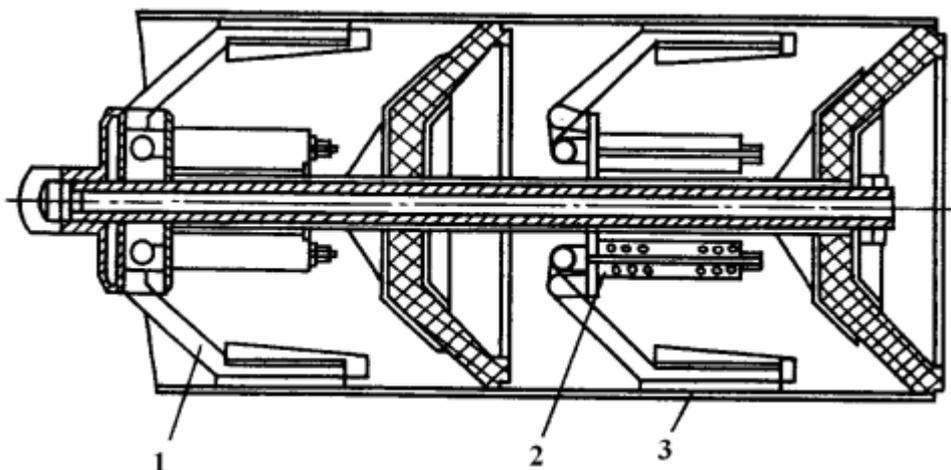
Конструктивная схема скребка: 1 – щеткодержатель; 2 – пружина; 3 – щетка
